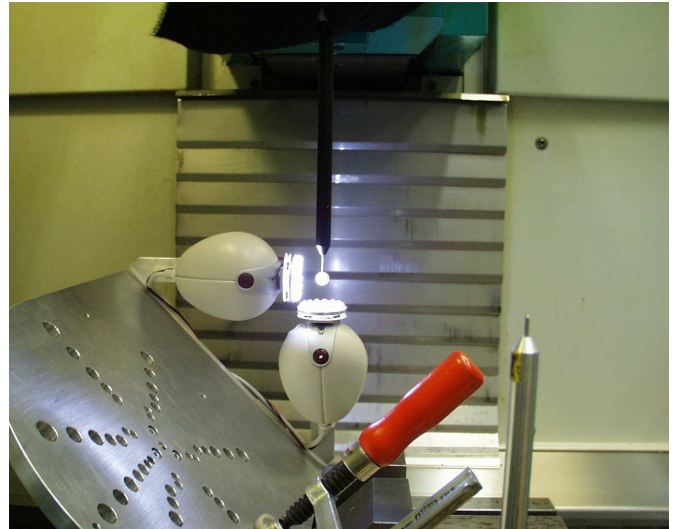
Meßwerkzeug bei Tests auf einer Fräsmaschine
